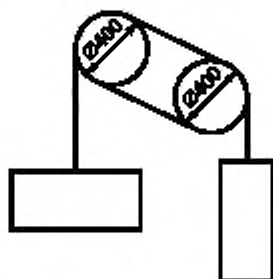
Прямая подвеска 1:1 (с двойным обхватом шкива канатом). Канатоведущий шкив с полукруглой канавкой
